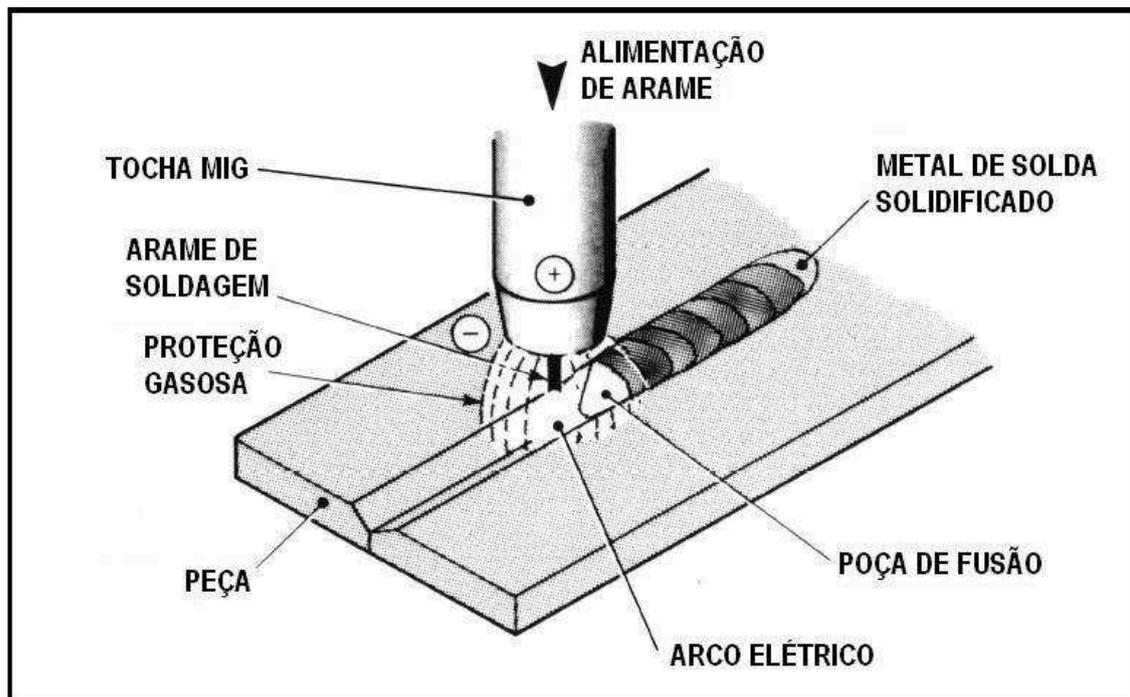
Processo básico de soldagem MIG/MAG (ESAB MIG).
